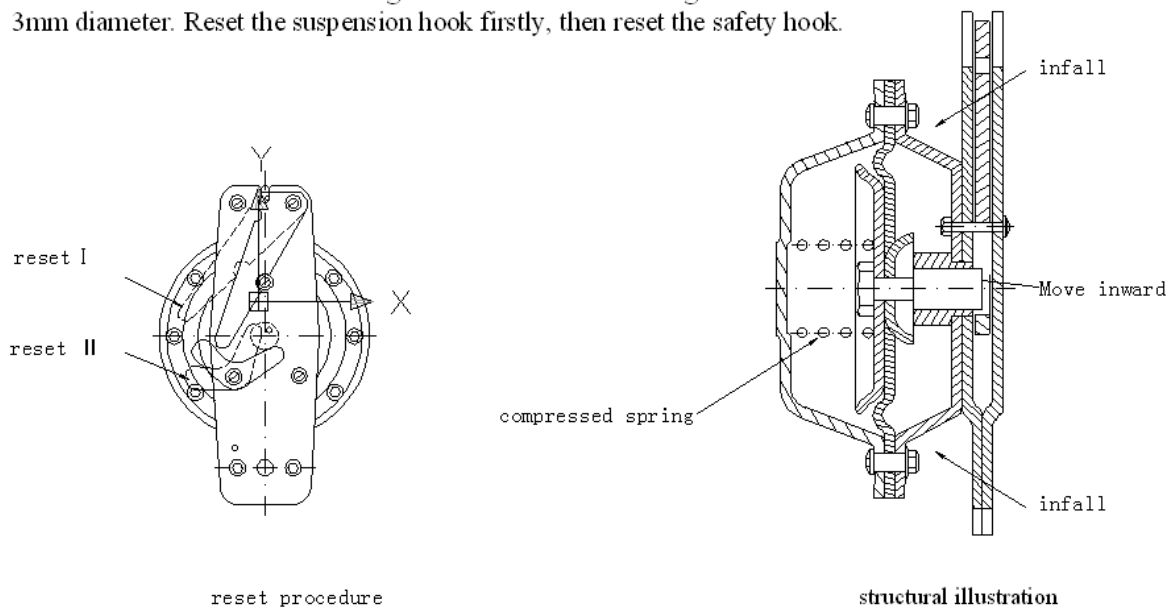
Повторная установка гидростатического разобщающего устройства и чертеж конструкции.
